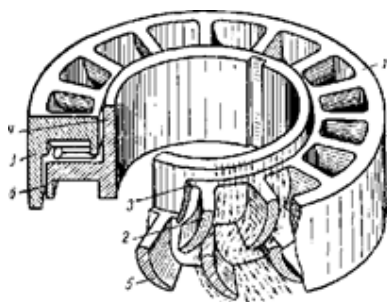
Общий вид статора и ротора турбобура и принцип действия турбины: 1 — наружное кольцо статора; 2 — лопатки статора; 3 — внутренний обод статора; 4 — внутреннее кольцо ротора; 5 — лопатки ротора; 6 — наружный обод ротора
